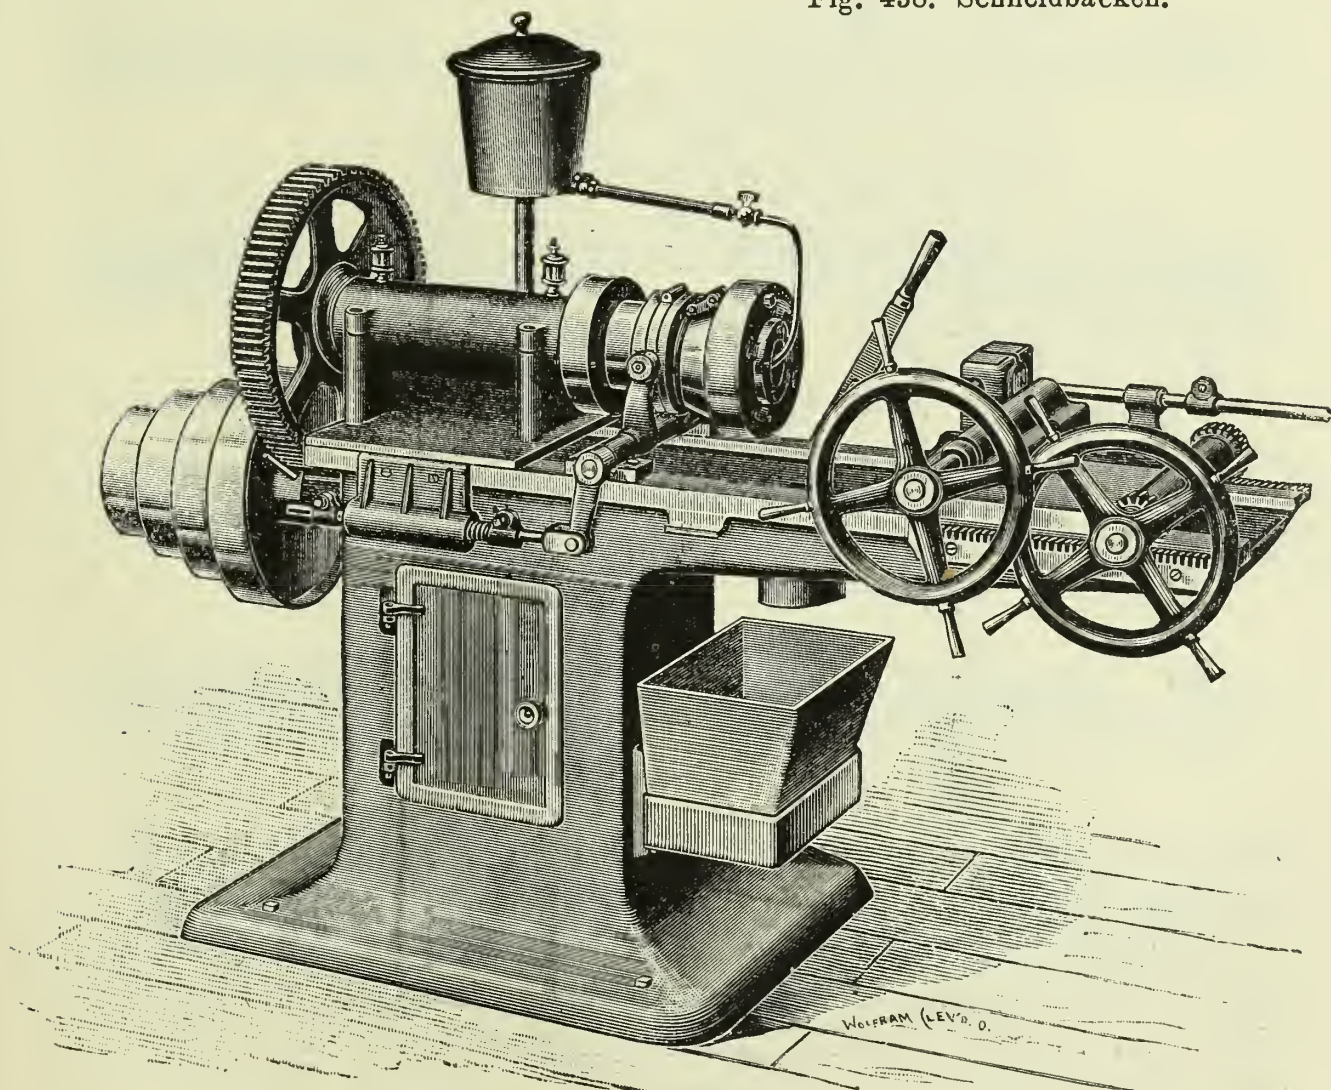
Schrauben-Schneidmaschine der 'Acme Machinery Co.
